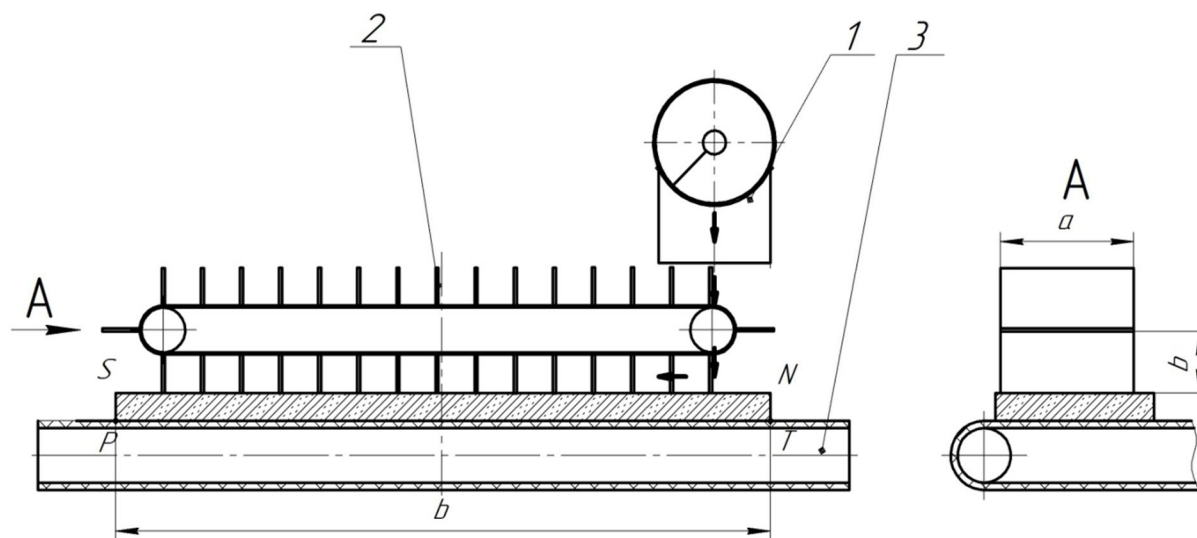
Схема работы скребкового разравнивающего устройства и ленточного транспортера:
